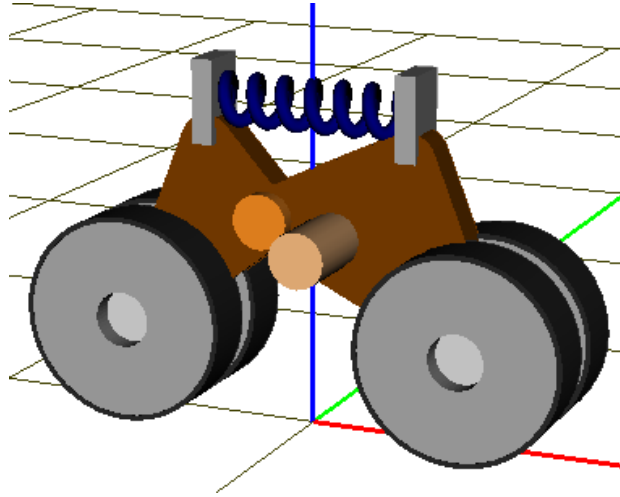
Балансирующая подвеска с двумя рычагами
